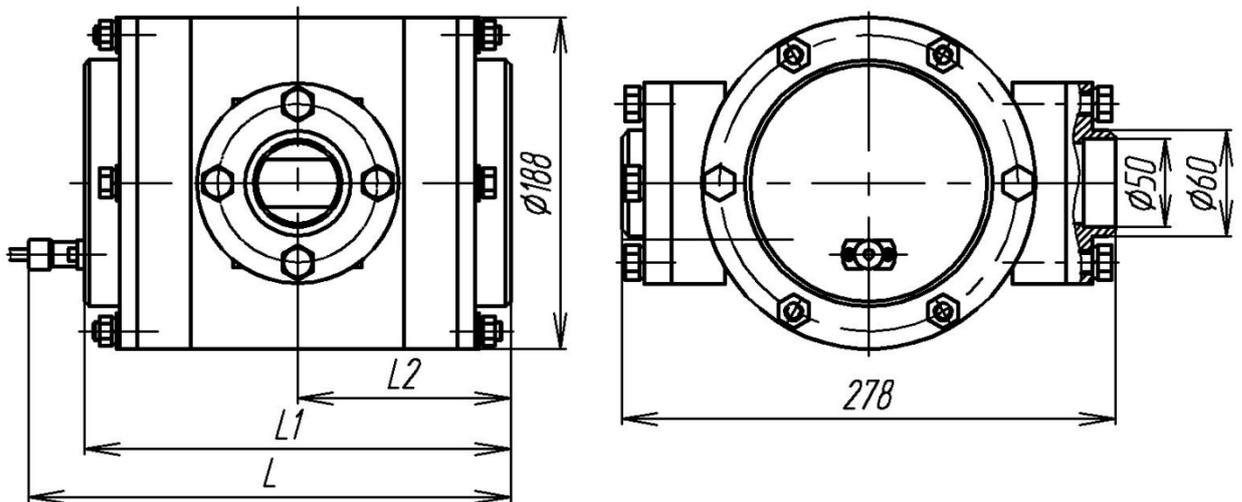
Габаритные и присоединительные размеры типа RVШ-PL
